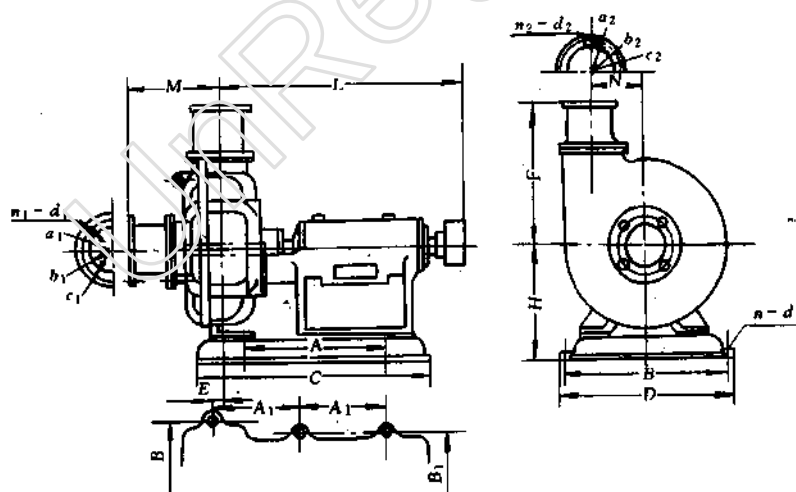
EXL-8A、6JH 型灰渣泵外形尺寸
